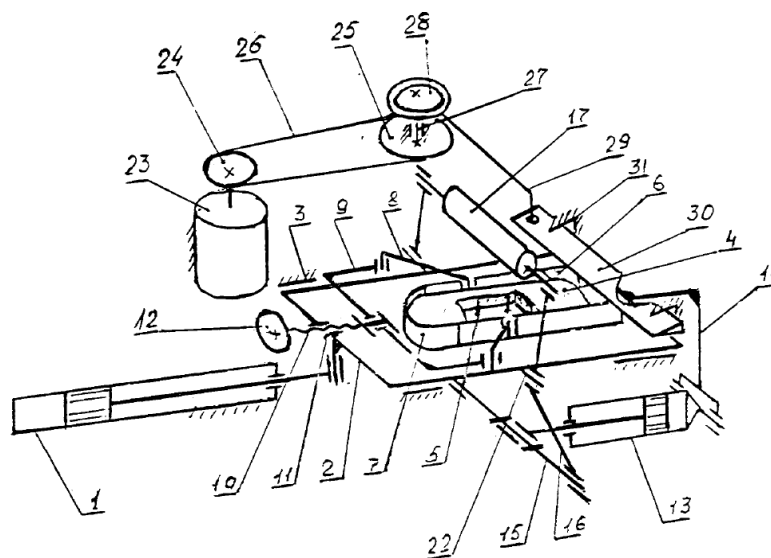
Кинематическая схема устройства для профильной обработки детали низа обуви
